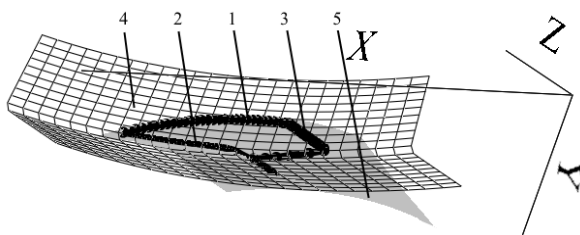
Пляма контакту фрези й кулачка розподільчого вала при обробці ділянки кулачка, центр якої збігається з центром кулачка
